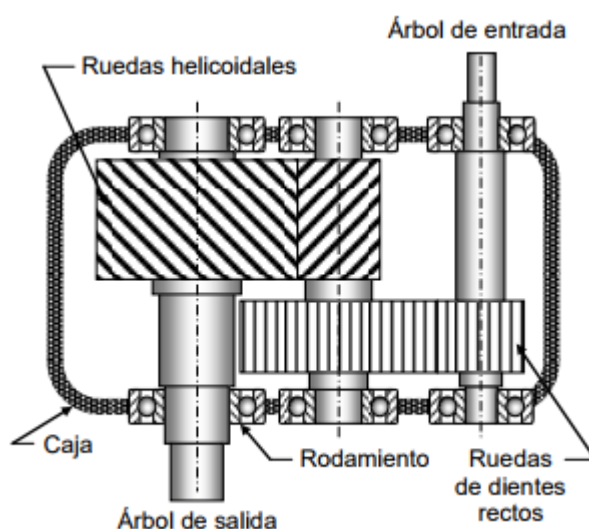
Sistema reductor mediante árboles de transmisión y engranajes
